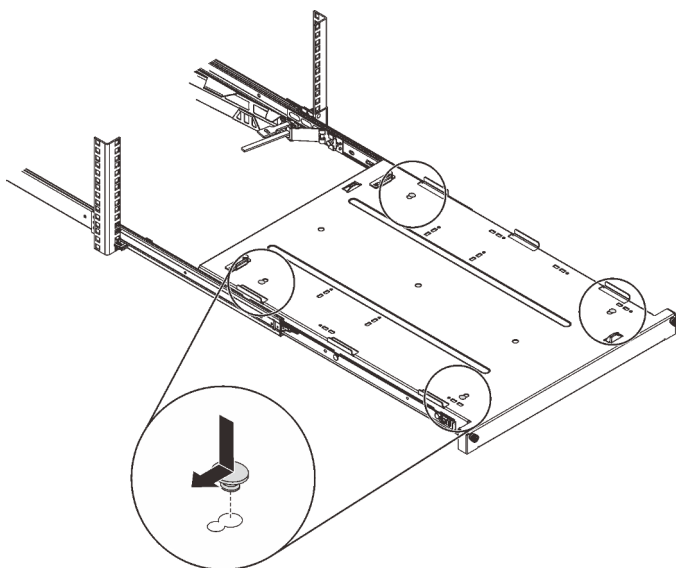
Installazione dei piedini di sicurezza in gomma nel vassoio
